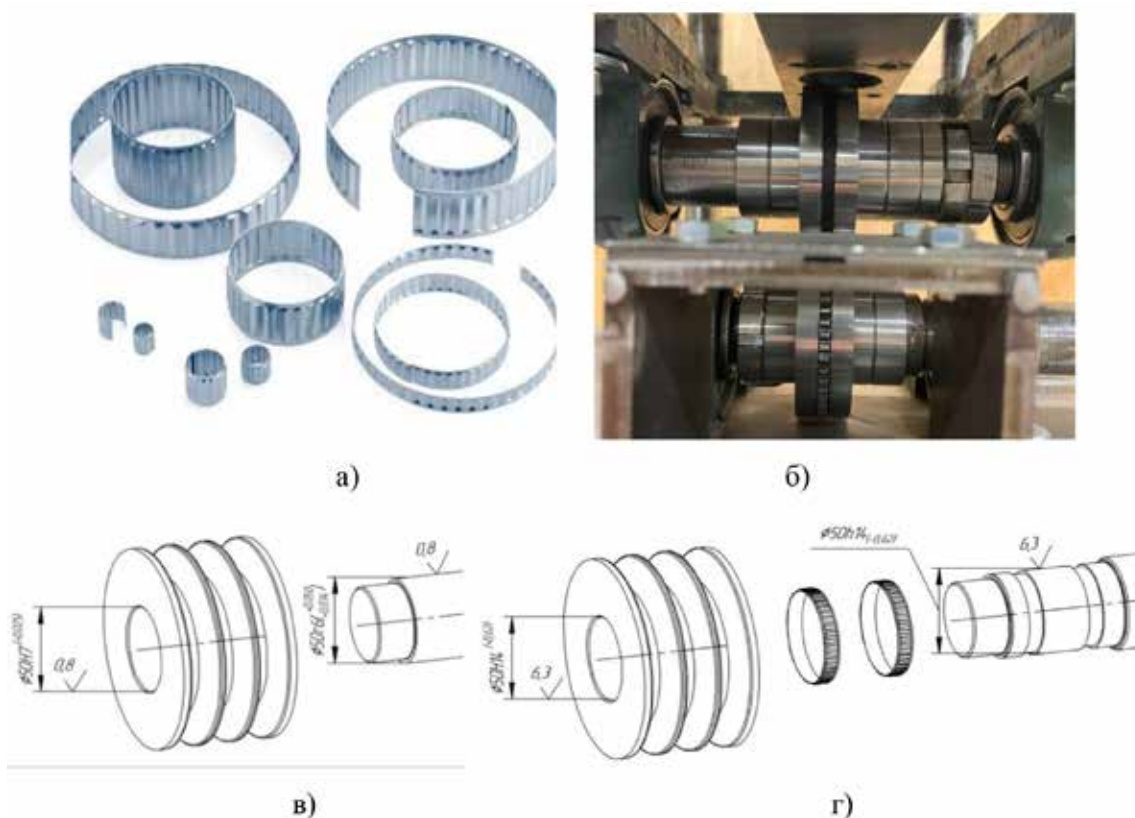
Разновидности демпферной ленты (а); узел формообразования волновых элементов, полупромышленный образец для экспериментальных исследований (б); крепление шкива на вал в натяг (в); крепление шкива на вал через демпфер (г)
